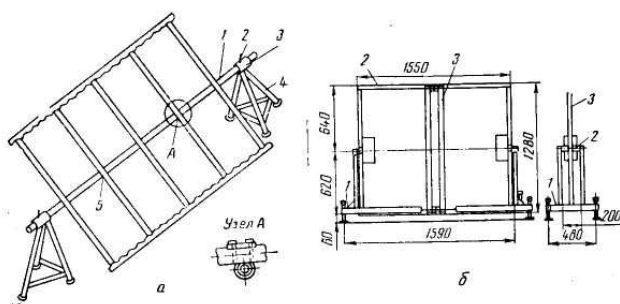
Контувучі-обертальники: а – для складання і зварки охолоджуючих батарей з готових деталей: 1 – орна труба; 2 – стопорний палець; 3 – опорна втулка; 4 – тринога; 5 – хомут; б – для складання і зварки охолоджуючих батарей з готових секцій конструкції ЦПКБ Главгепродмонтажа: 1 – основа; 2 – поворотна рама; 3 – притискна рама.
